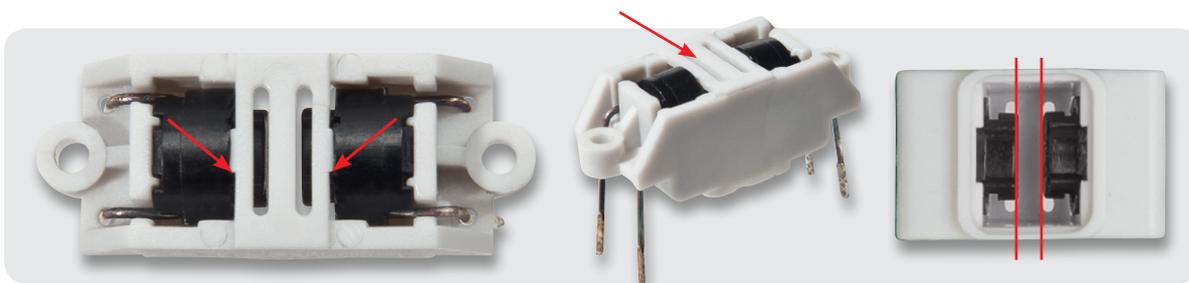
Die Taster der Schaltwippe sind wie abgebildet in die Halterung zu montieren.
